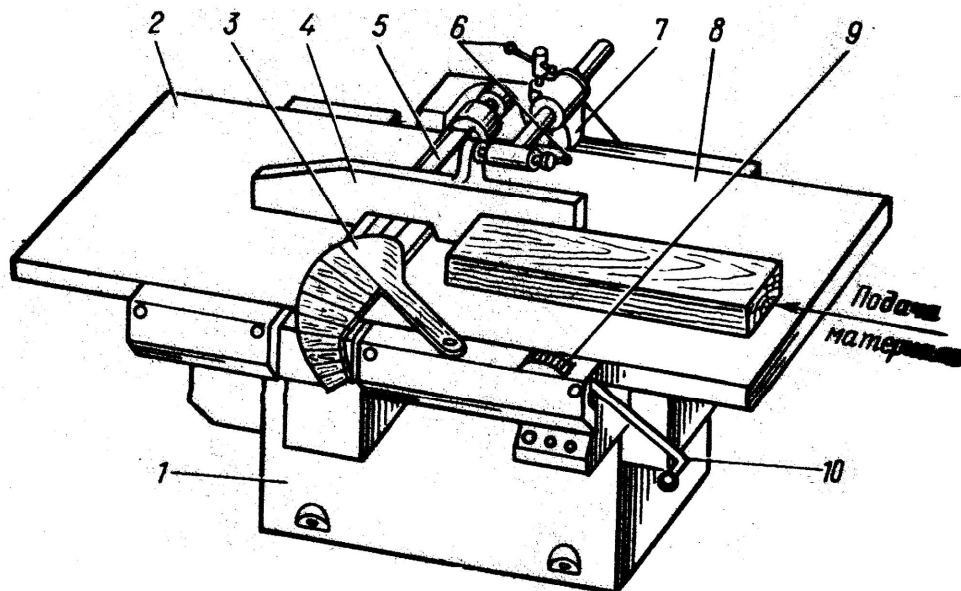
Верстат для обробки деревини: 1 – станина; 2 – задній стіл; 3 – огорожа; 4 – направляюча лінійка; 5 – ножевий барабан; 6 – фіксатор кріплення направляючої лінійки; 7 – кронштейн; 8 – передній стіл; 9 – шкала; 10 – рукоять налагодження столі по висоті.
